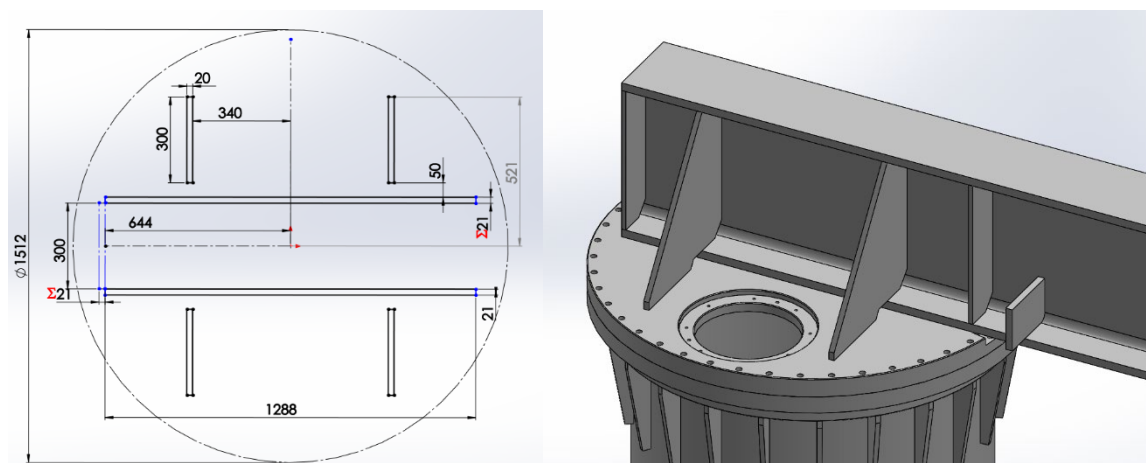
Esquema de las soldaduras de cálculo.
